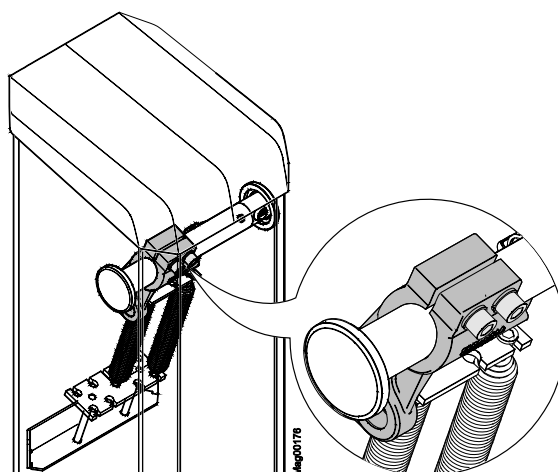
Innensechskantschrauben am Klemmhebel lösen
